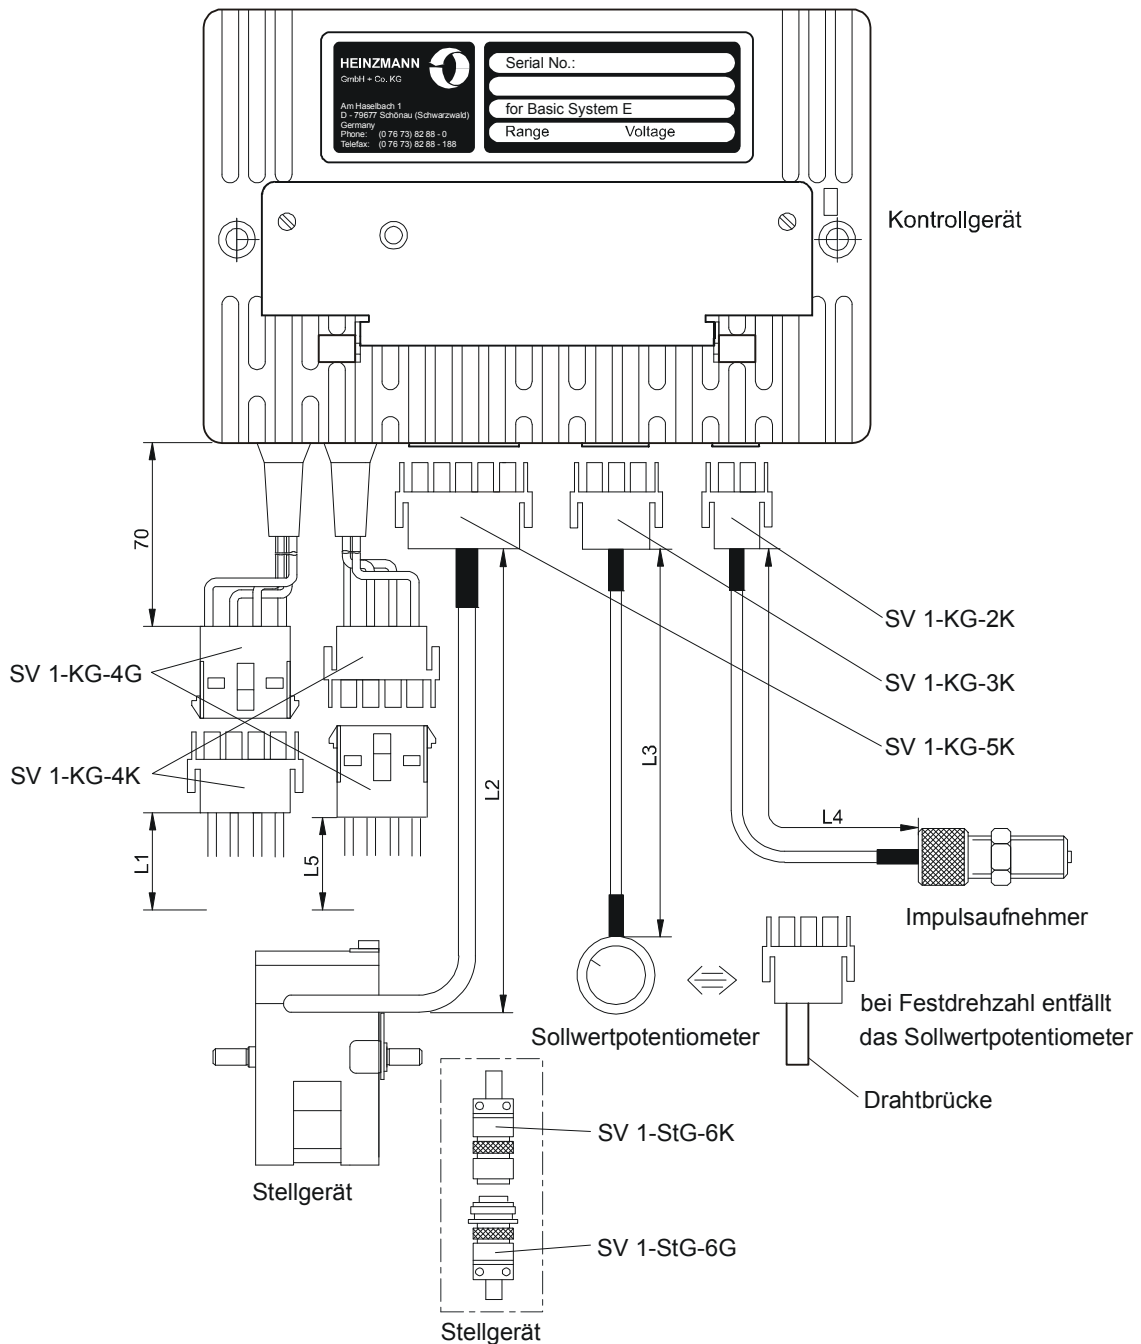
Kabelbaum mit Steckerbezeichnungen
